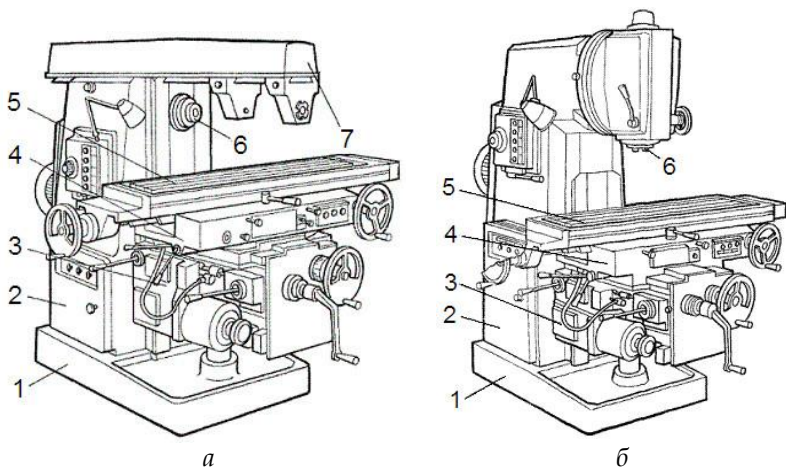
Консольный горизонтально-фрезерный (а) и консольный вертикально-фрезерный (б) станок: 1 – плита основания; 2 – станина; 3 – консоль; 4 – салазки; 5 – стол; 6 – шпиндель; 7 – хобот
